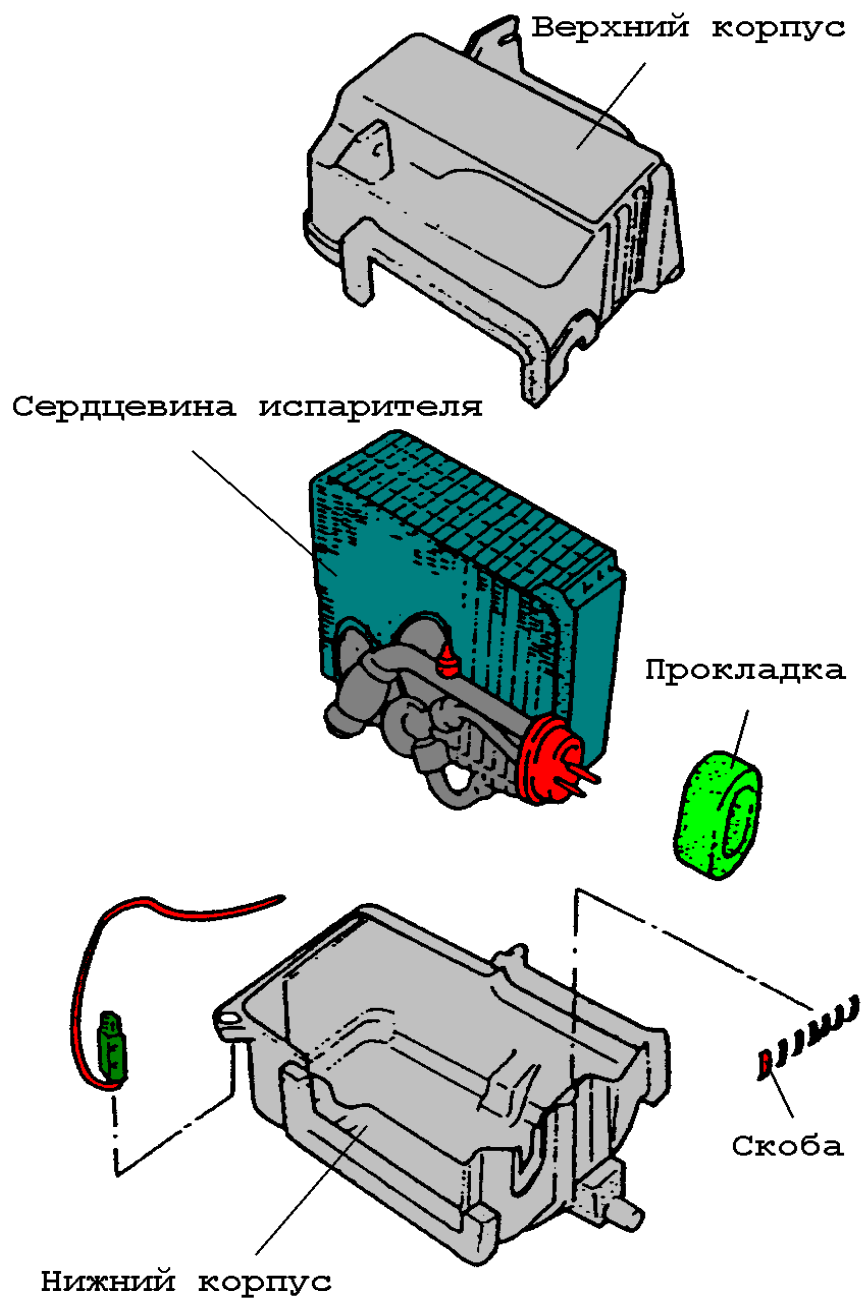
Приклад типового випарника системи кондиціювання із корпусом.
